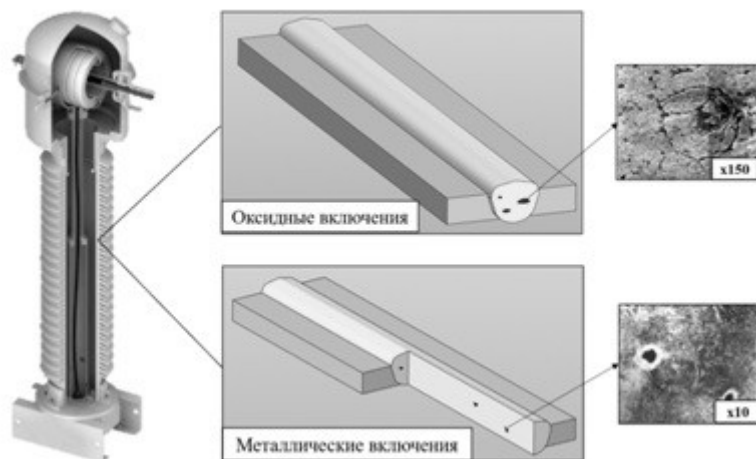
Дефекты сварного соединения алюминиевого корпуса
